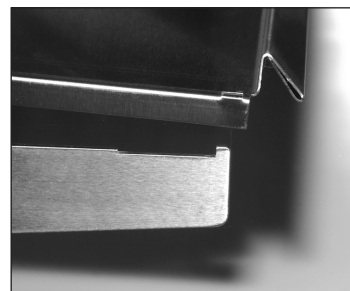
Haak de plankdragers op de gewenste hoogte in de pilasters.
